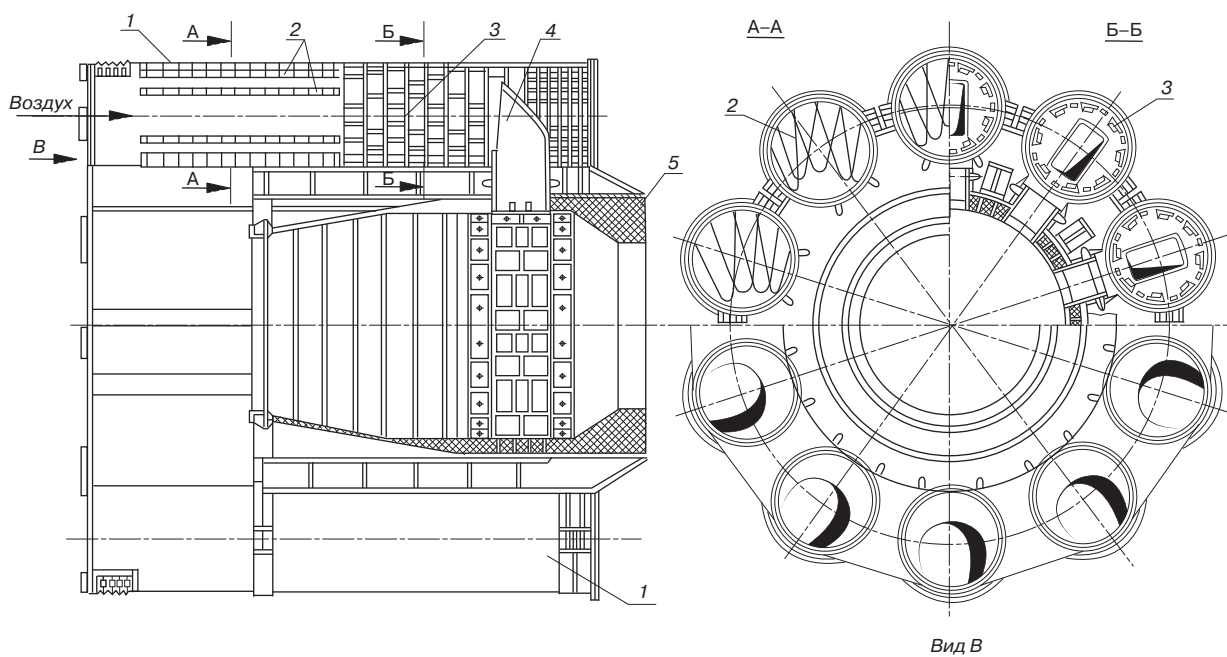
Рекуператорный холодильник извести вращающейся печи $\varnothing 2,5 \times 75$ м: 1 – барабаны извести; 2 – полки; 3 – футеровочные плиты из жаропрочной стали; 4 – течи из жаропрочной стали; 5 – корпус печи
